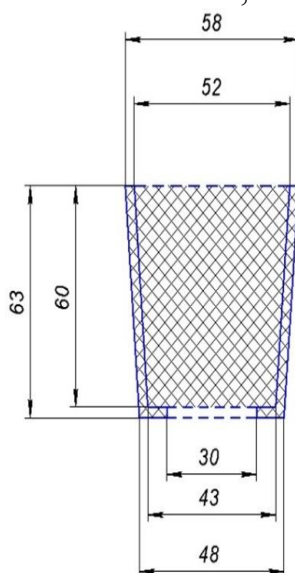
Внешний вид и размеры стандартного стаканчика для определения величины эффекта подкормки
